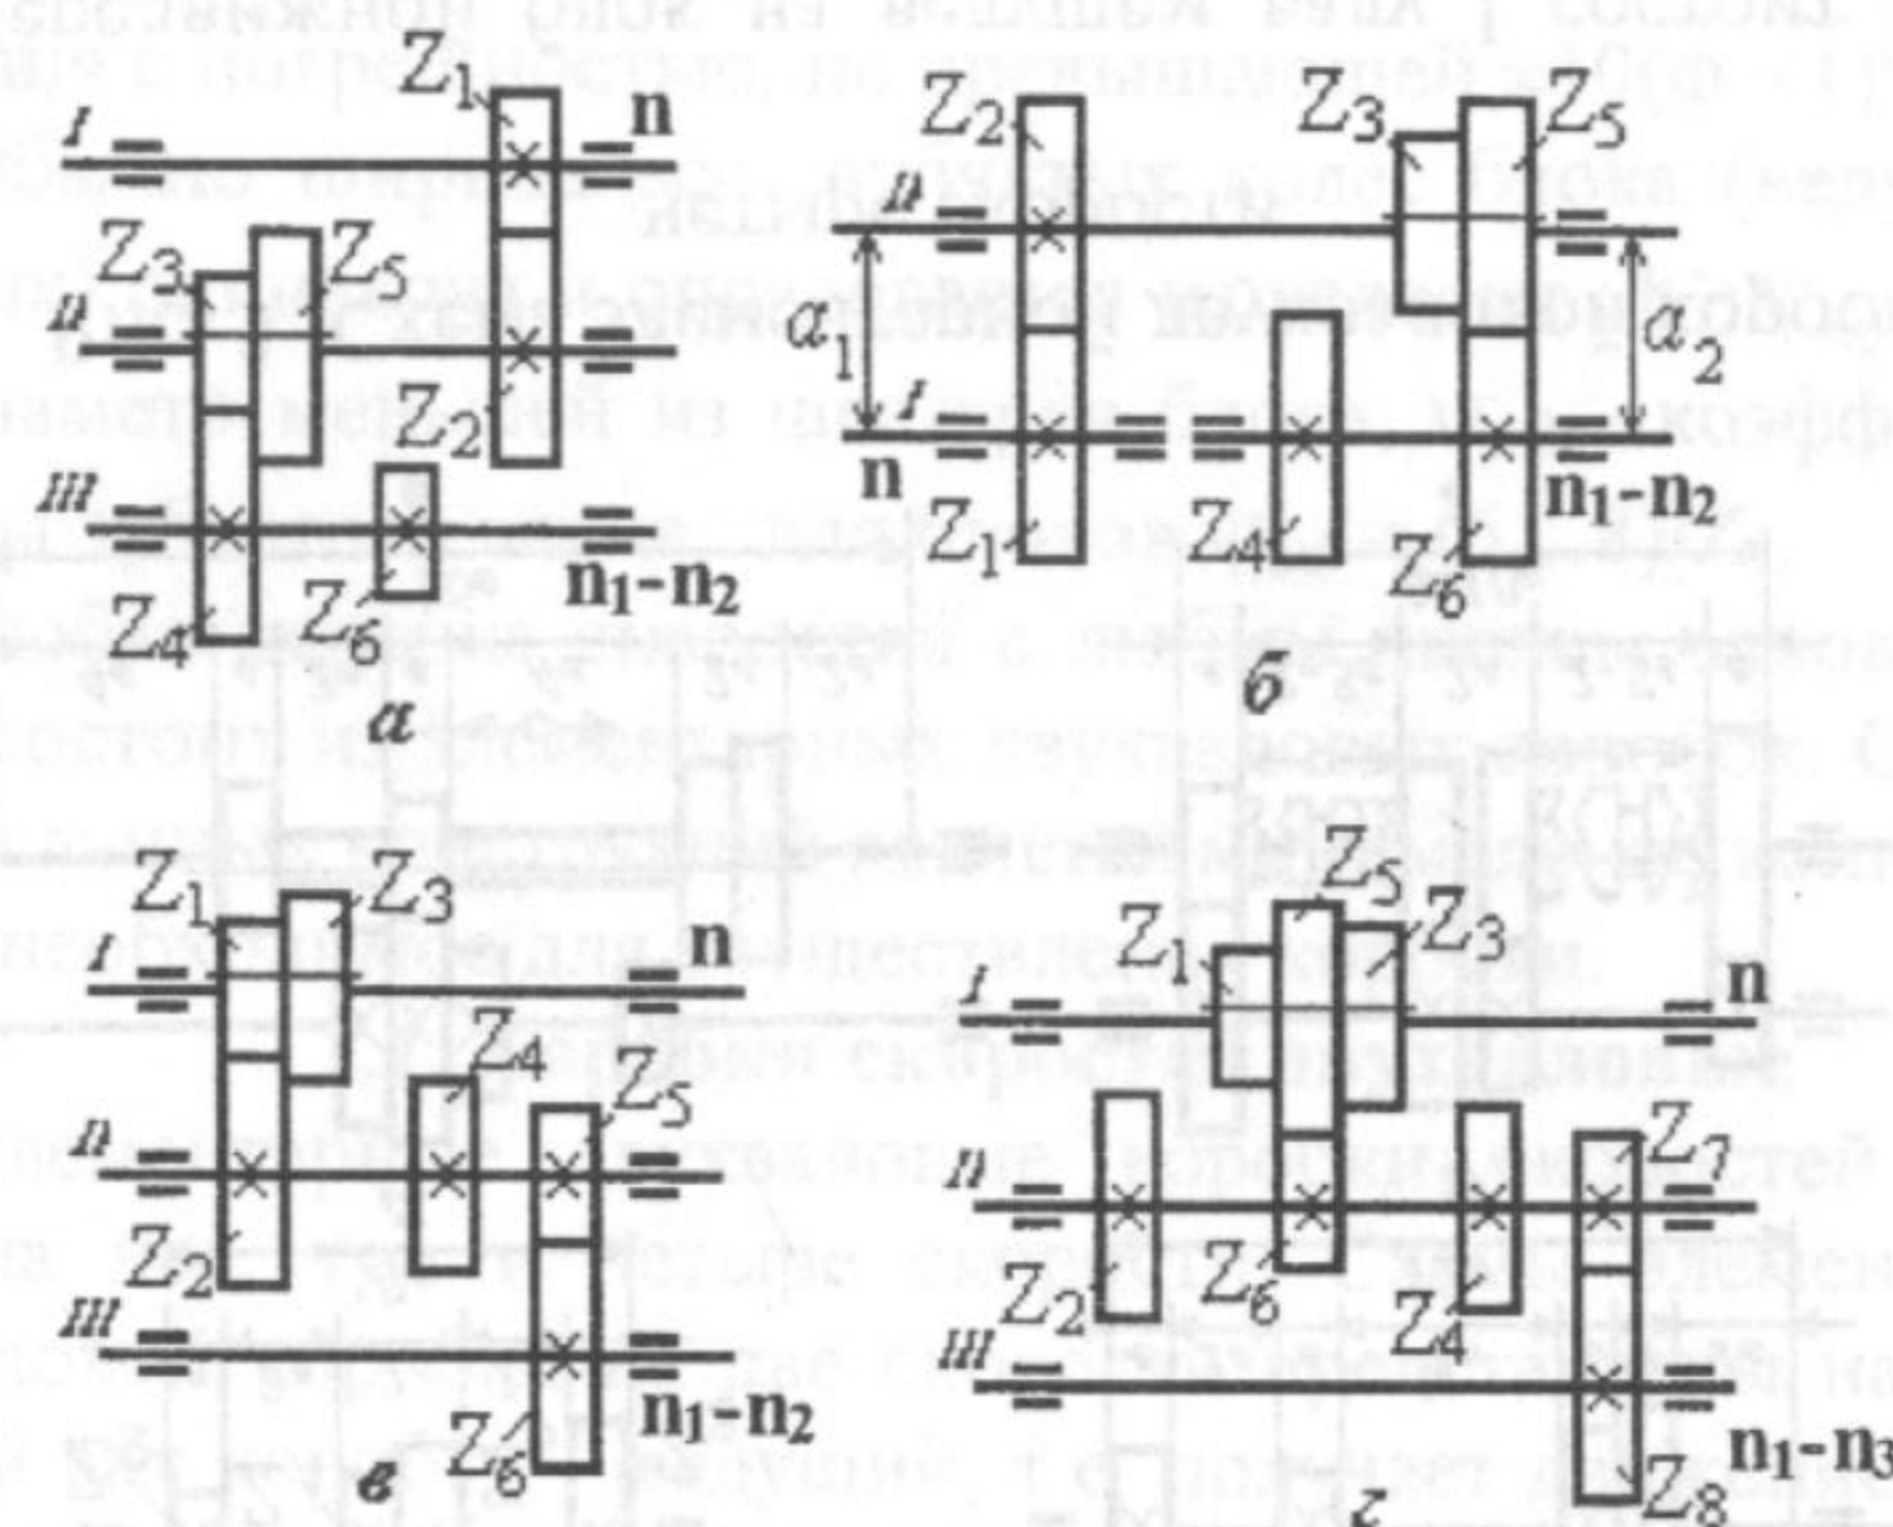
Схемы трехваловой коробки на две и три скорости с дополнительной цилиндрической передачей
